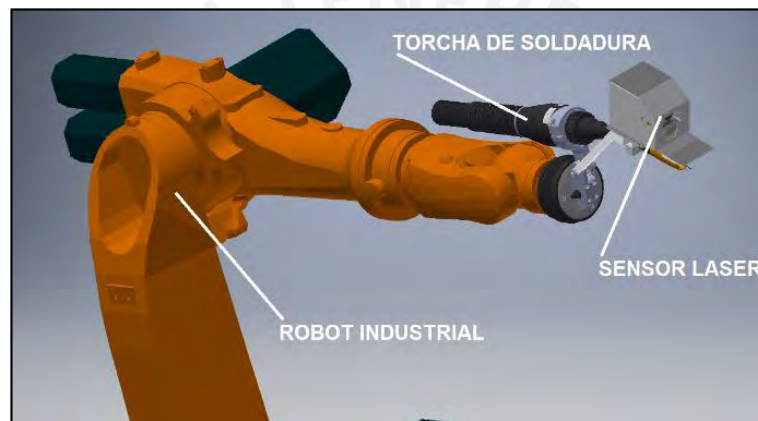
Propuesta de diseño de sistema automatizado de soldadura
